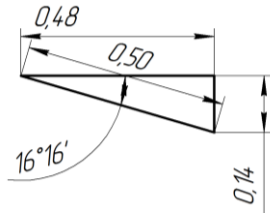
Кресленник схеми визначення радіуса та кута розташування центра ваги борштанги без противаги
